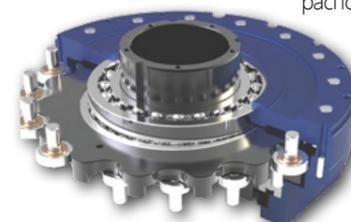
Модель планетарно-цевочного редуктора в разрезе
